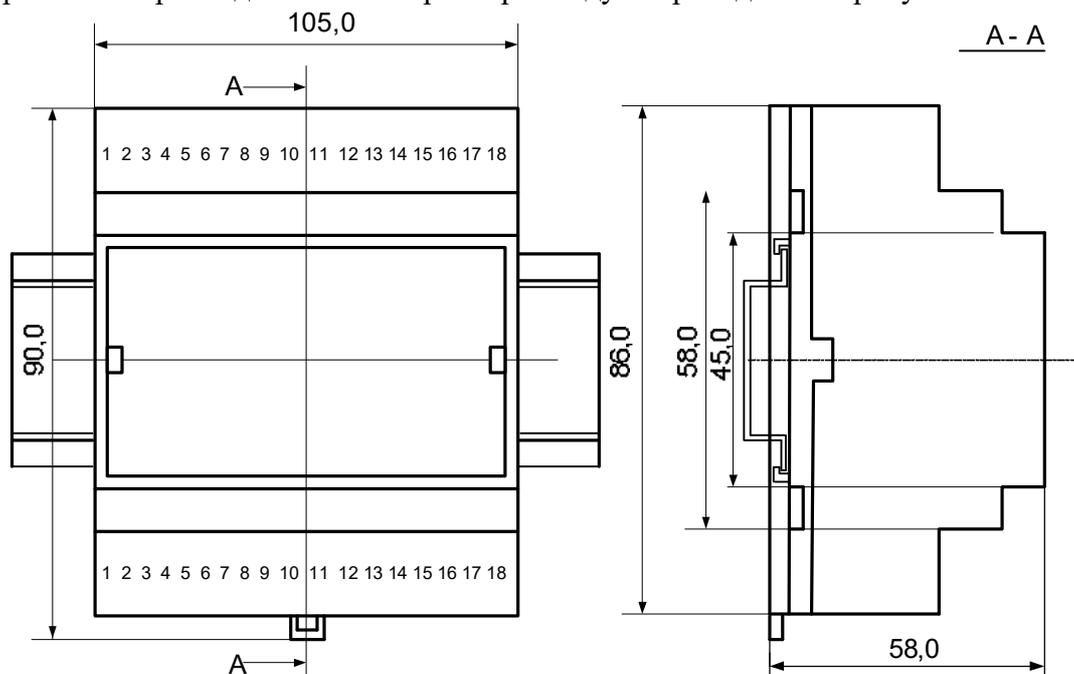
Габаритные и присоединительные размеры модуля
